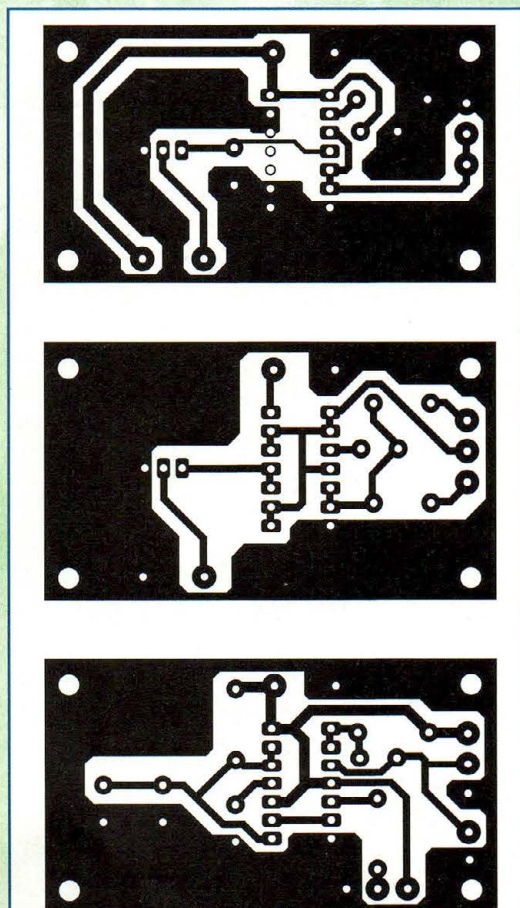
Reproduction des circuits imprimés à l'échelle 1 vu du côté des soudures.
